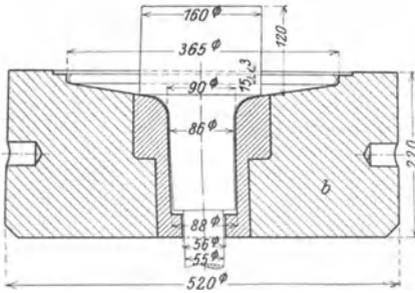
Gesenk zum Ausschlagen des Tellers.
